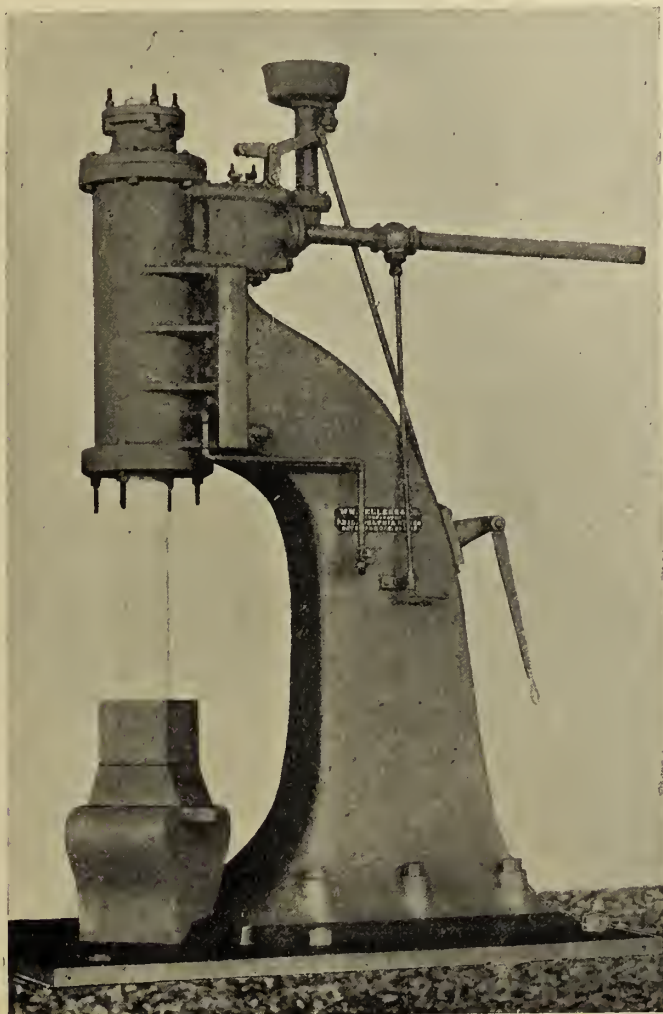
Pilon Sellers pour soudure de longerons.
